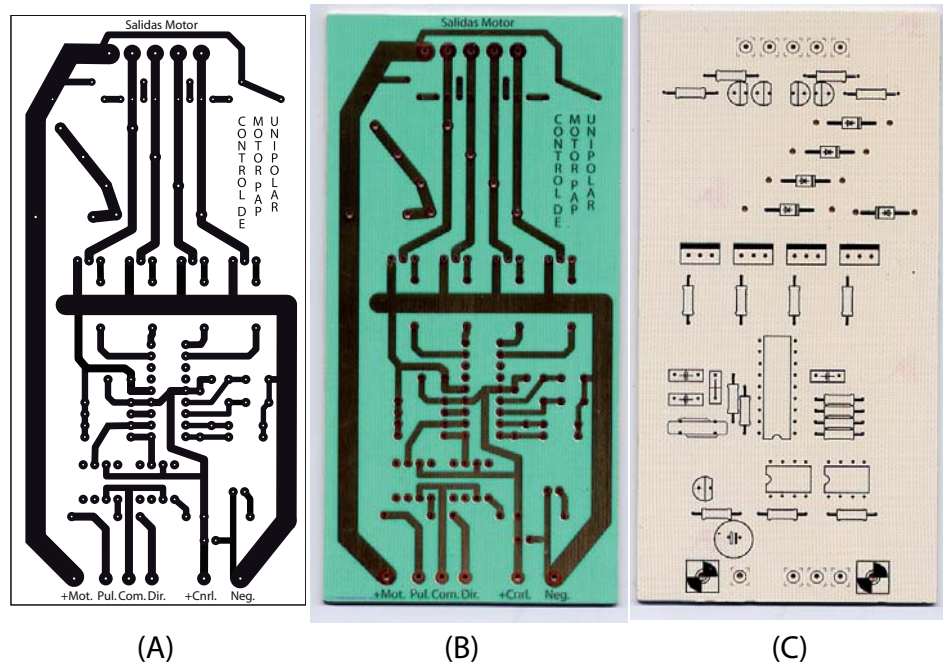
Diseño hecho en Adobe Illustrator (A), circuito impreso con máscara antisoldadura (B) y la impresión de la máscara de componentes en el lado opuesto del circuito impreso (C).
